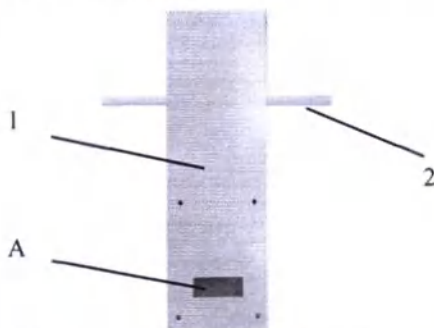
Стойка модуля нагревателя. Вид спереди.
